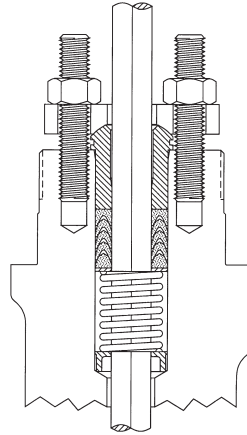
Einzel-PTFE V-Ring-Packung
